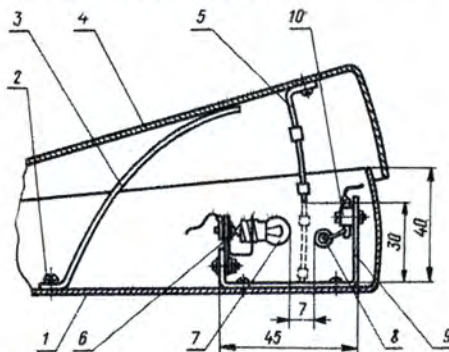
Конструкция педали. 1 — корпус; 2 — винт крепления пружины; 3 — плоская пружина; 4 — крышка; 5 — кронштейн с экраном переменной прозрачности; 6 — держатель лампы накаливания; 7 — лампа накаливания 3,5 В/0,26 А; 8 — диод Д2В; 9 — скоба крепления лампы и диода; 10 — изолятор-держатель диода.
